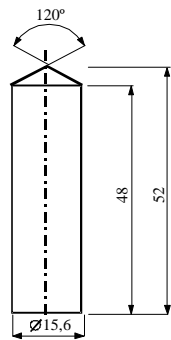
Piston cylindrique en bronze, dimensions en mm
